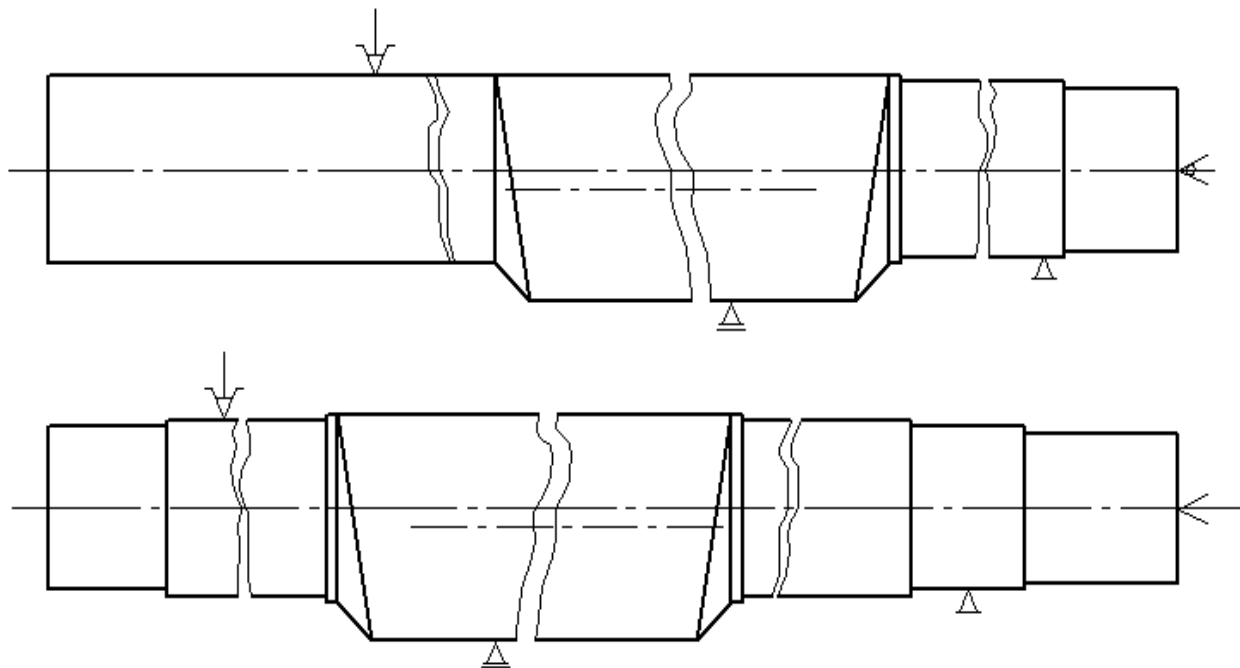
Схема базування вала на токарну чорнову обробку
